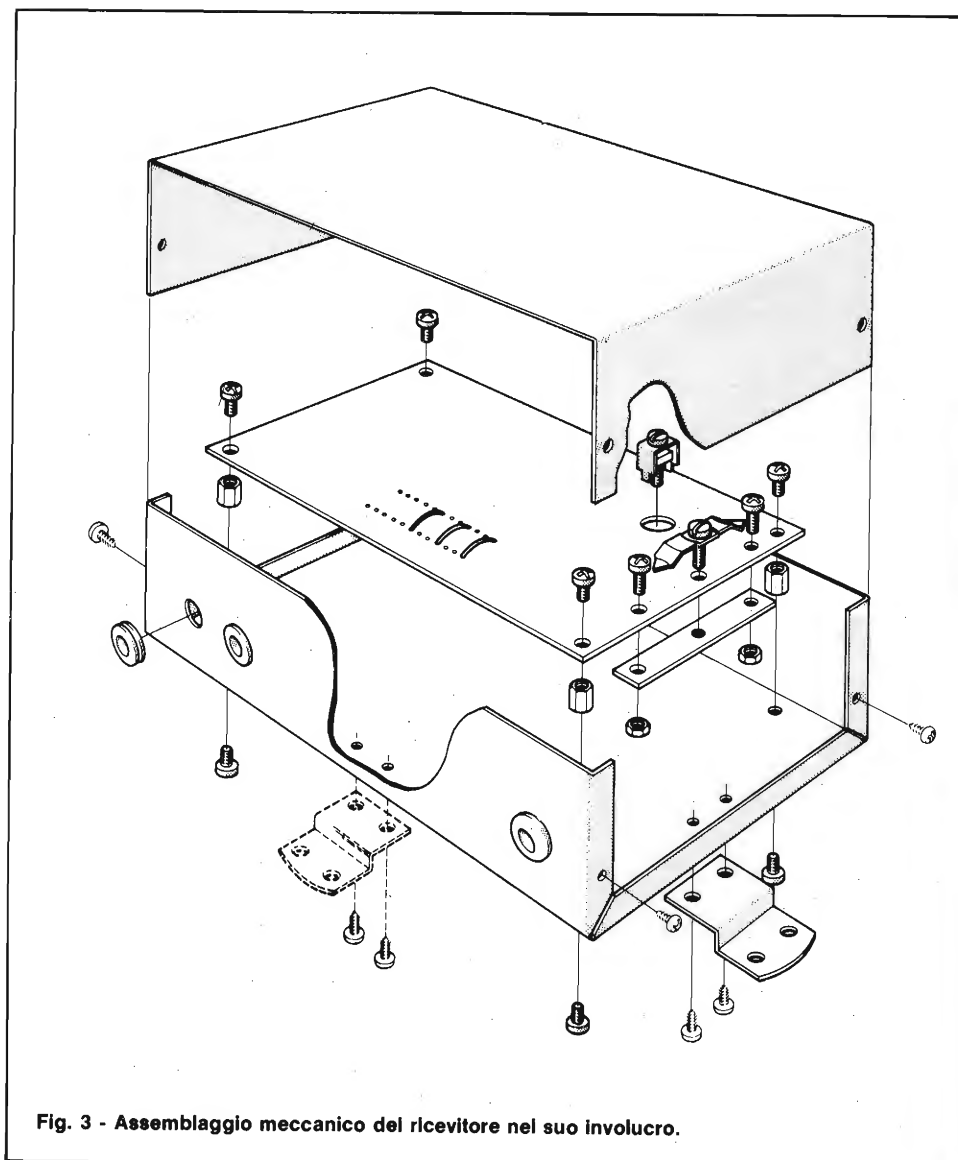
Assemblaggio meccanico del ricevitore nel suo involucro.
